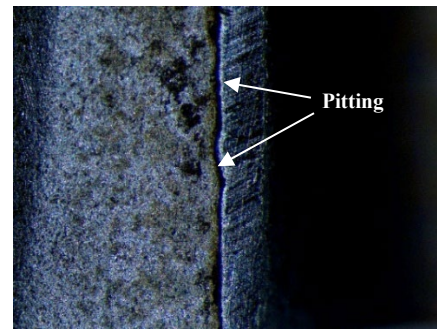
Fisuras y grietas en pieza del conector Straight Joint
